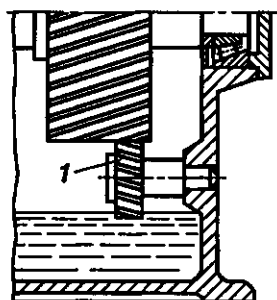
Смазка с помощью вспомогательного колеса: 1 – колесо
